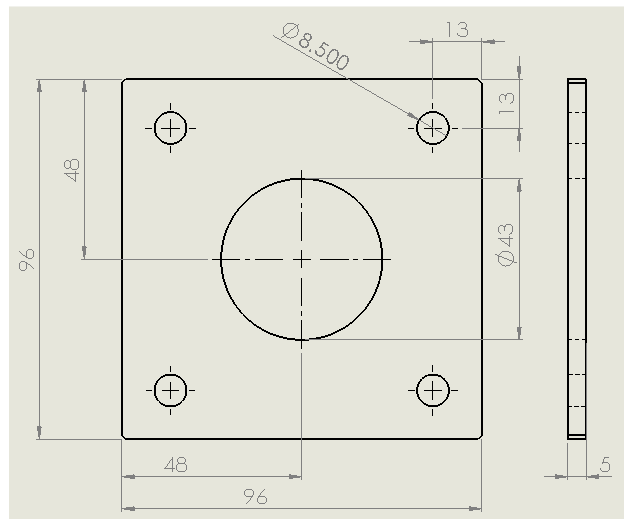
Medidas de placa (cotas en mm)
